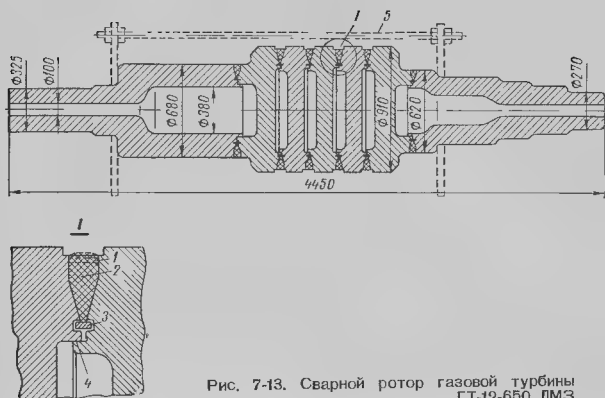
Сварной ротор газовой турбины ГТ-12-650 ЛМЗ
